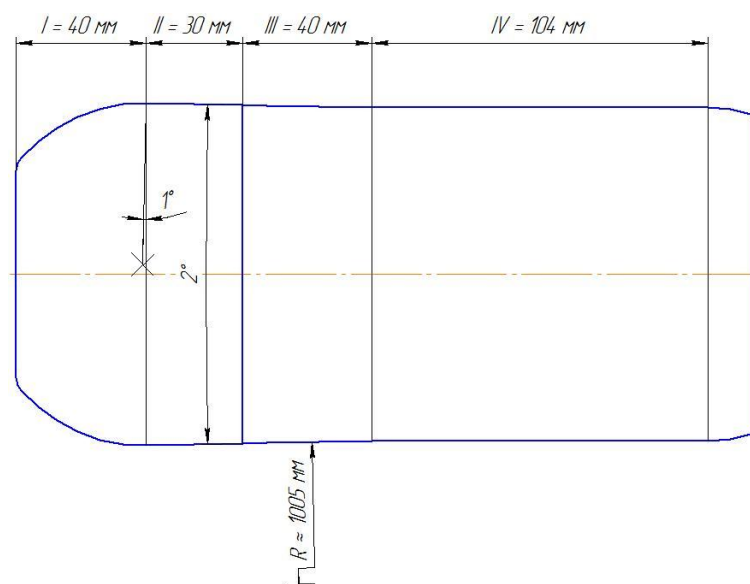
Калибровка оправки трехвалкового обкатного стана для ведения процесса обкатки с уменьшением диаметра черновой трубы
